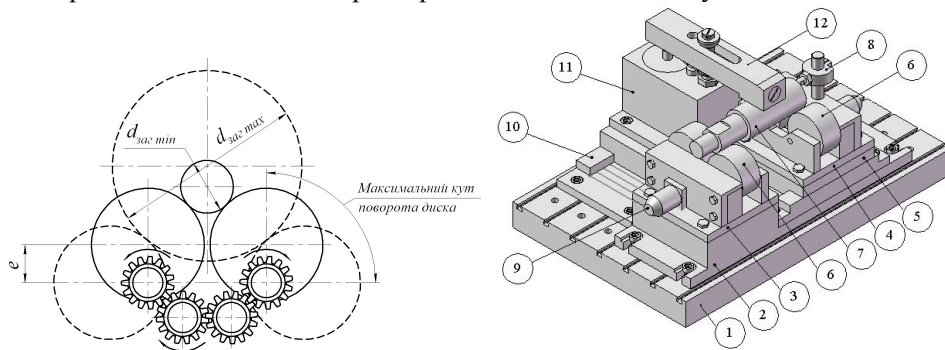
Універсально-збірний переналагоджуваний пристрій: а – схема механізму регулювання установочних елементів; б – компоновка УЗПП
